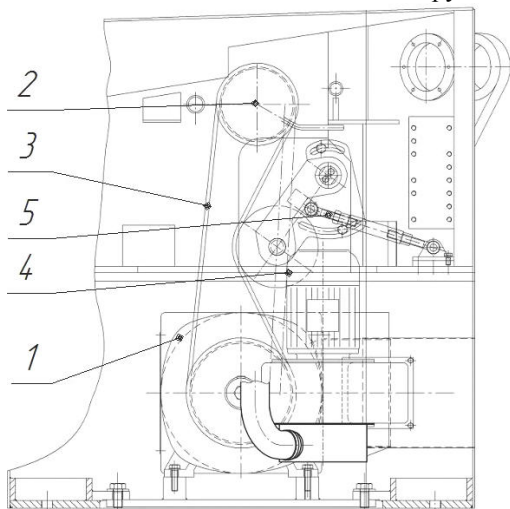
Натяжное устройство приводных ремней ножевого вала куттера Laska KUX 500 V: 1 – электродвигатель; 2 – ножевой вал; 3 – ремень; 4 – натяжной ролик; 5 – регулировочный шток
